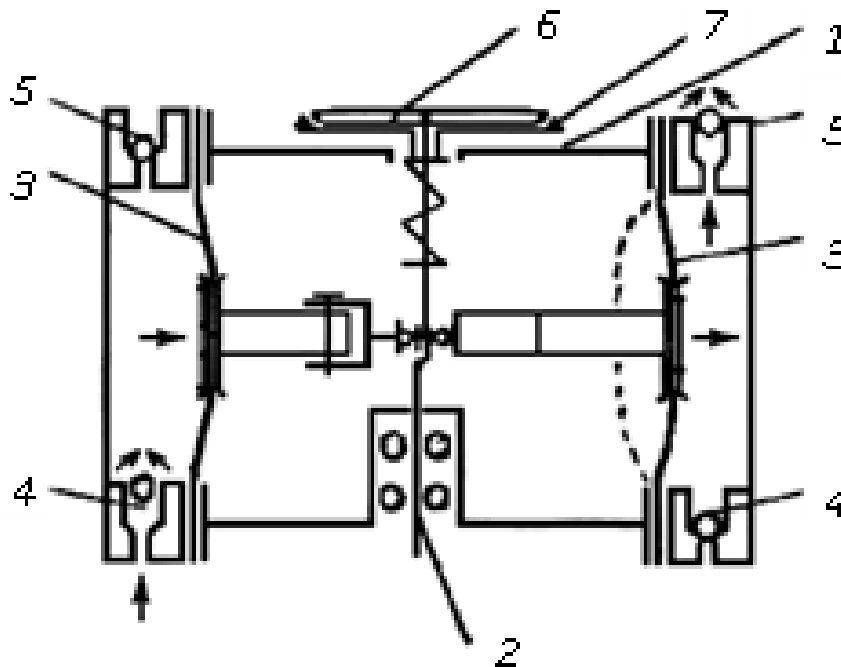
Схема роботи насоса-дозатора робочої рідини:
